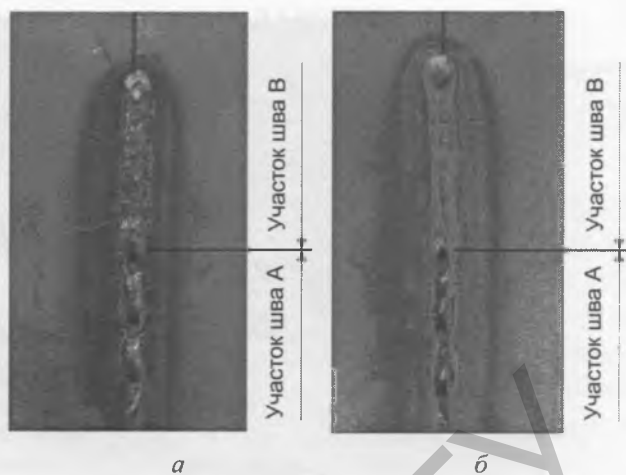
Стыковой сварной шов, выполненный механизированной сваркой в защитном газе: *a* – лицевая сторона шва; *б* – обратная сторона шва
